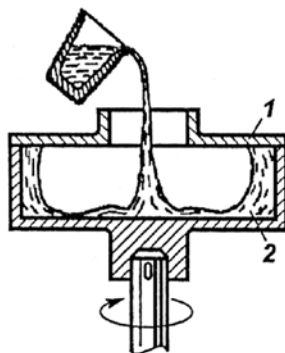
Центробежное литьё: 1 – центробежная изложница; 2 – расплавленный металл
